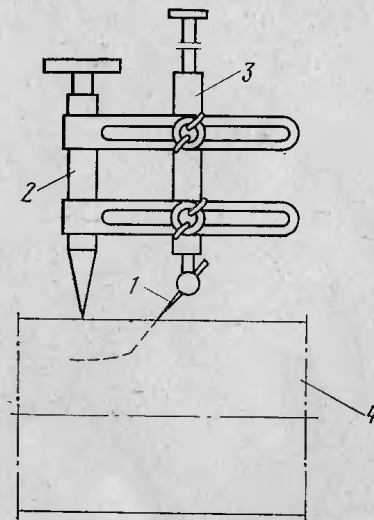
Универсальный циркуль для разметки отверстий-врезок в трубах.
